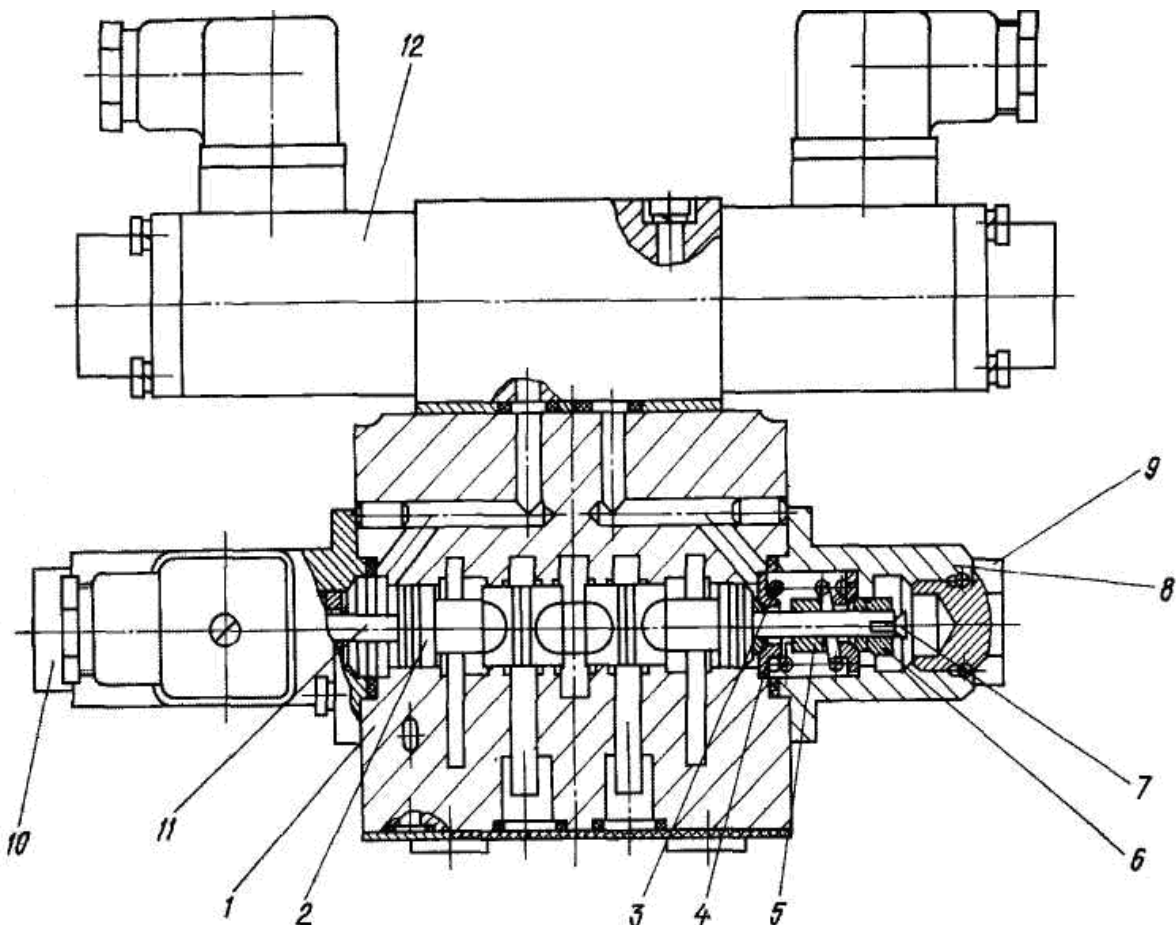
Конструкція гідророзподільника типу РР-10: 1 – корпус; 2 – запірно-регулюючий елемент; 3 – пружина; 4 – шайба; 6 – гайка; 7 – гвинт; 8 – кришка; 9 – пробка; 10 – датчик зворотного зв'язку; 11 – ось; 12 – керуюча ступінь
